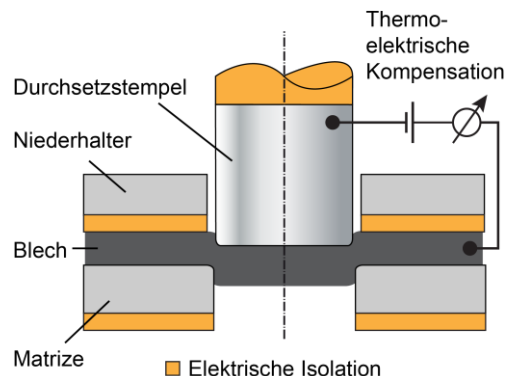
Messprinzip Werkzeug-Werkstück-Thermoelement
